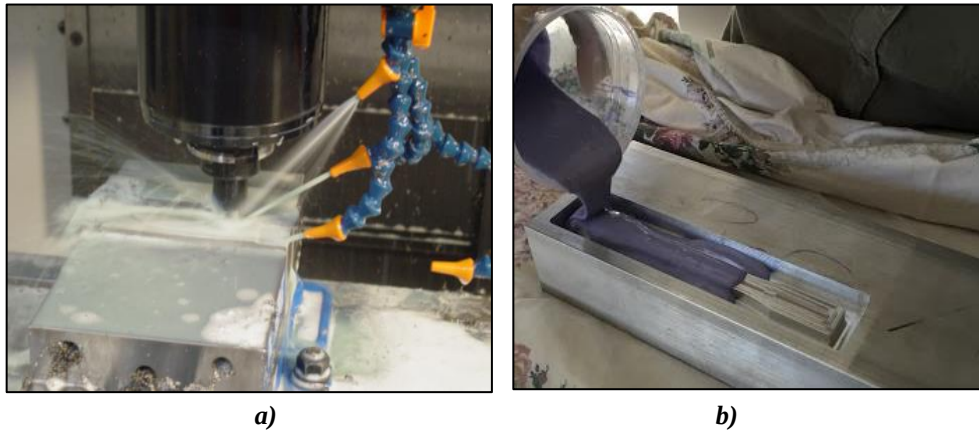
a) Maquinado de aluminio positivo; b) Manufactura de moldes negativos de silicón.
